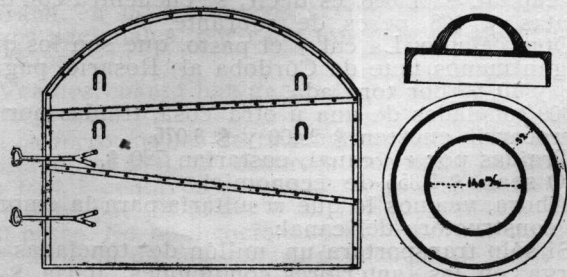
Diafragma.—Fig. 27: Corte transversal y planta de una campana
